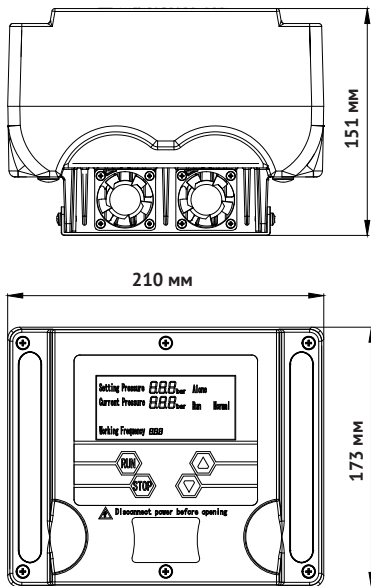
Габаритные размеры FCP-1.5–2.2LT
